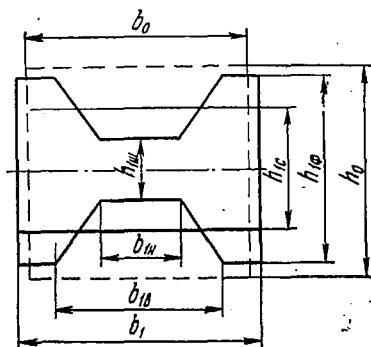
Сечение полосы после прокатки квадратной заготовки в разрезном калибре
